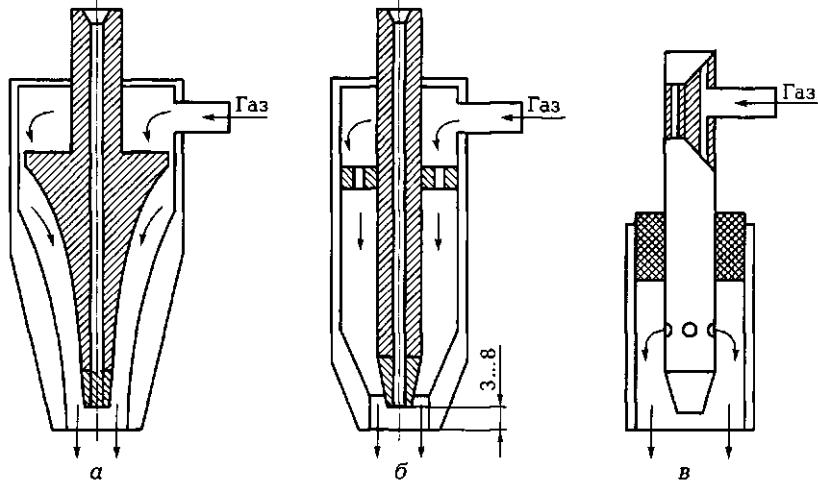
Схемы подачи защитного газа в сварочные горелки:
